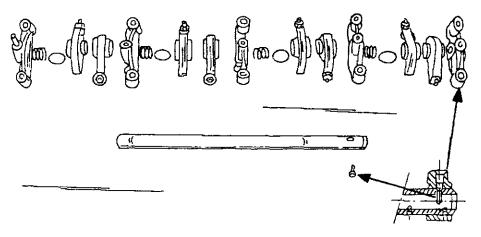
Монтажный чертеж вала коромысел. На нижнем правом разрезе показан винт, скрепляющий детали. Слева видно распорное кольцо.
